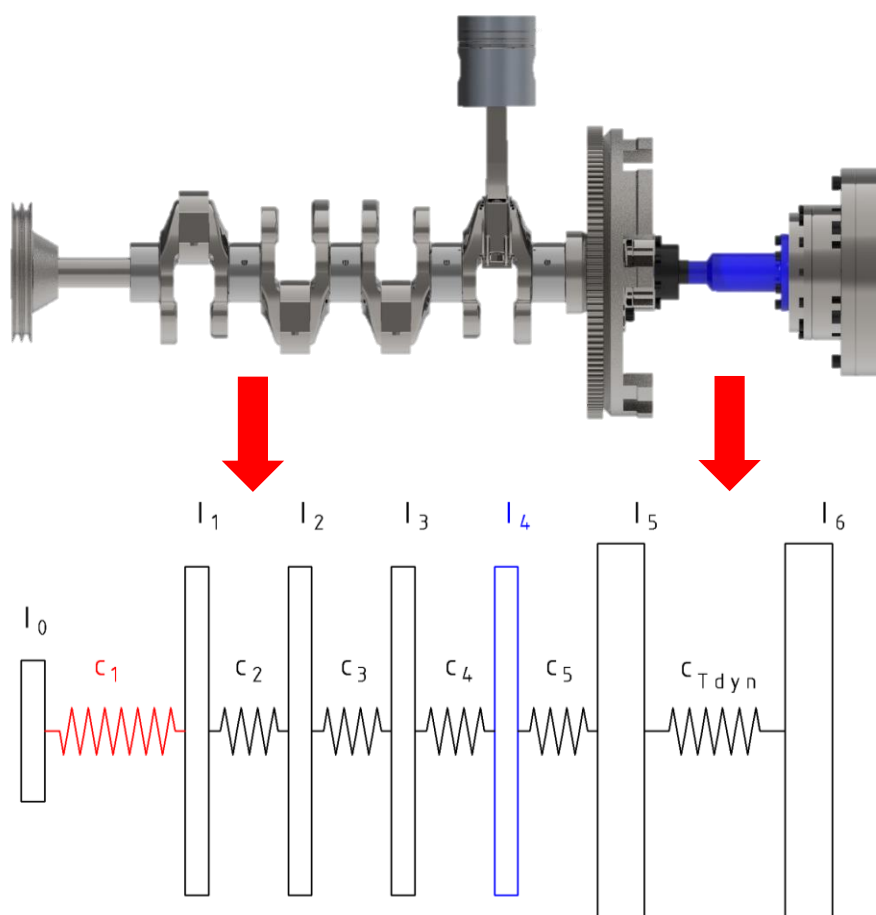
Spojovací hriadeľ s pružnou spojkou a adaptérmi
